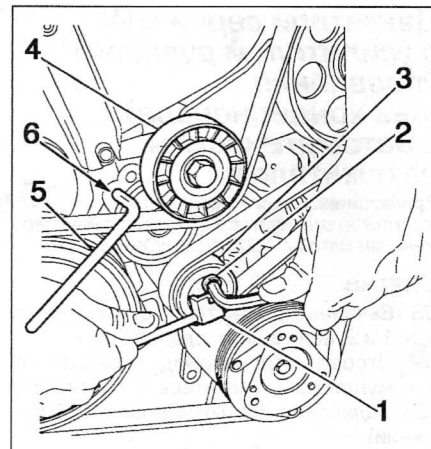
Регулировка ремня привода вспомогательных агрегатов (двигатели 2.0 л)
